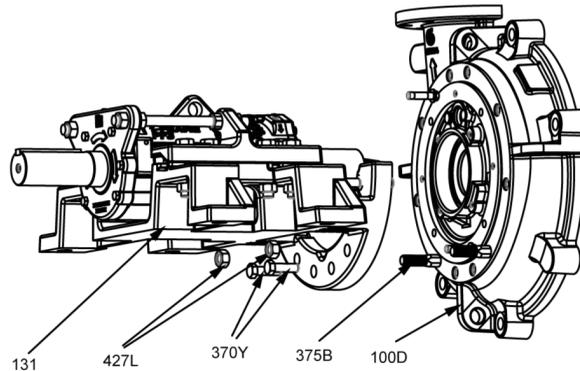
Dépose du couvercle d'étanchéité et de l'ensemble demi-corps de presse-étoupe
